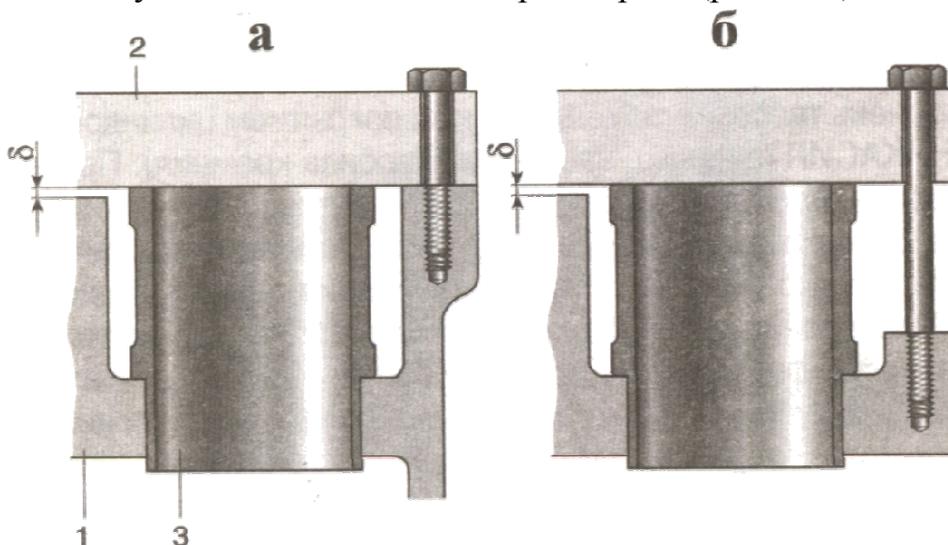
Схема установки болтов крепления головки блока с «мокрыми» гильзами:
